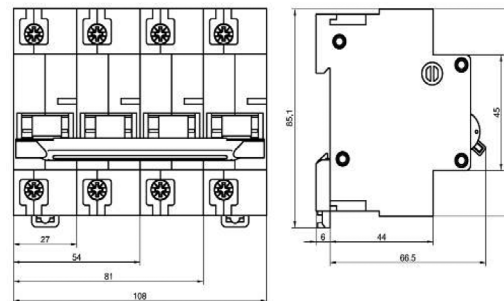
Габаритные, установочные, присоединительные размеры выключателей.
